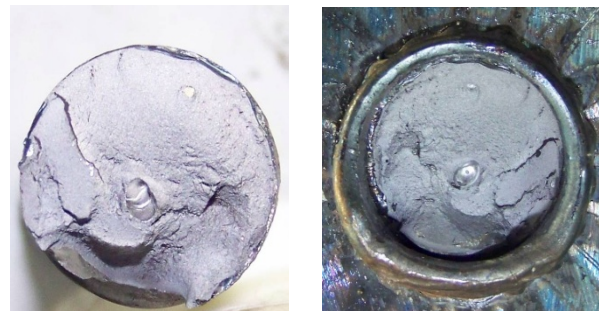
Внутрішні дефекти зварювання (пори та несплавлення) в третьому зразку
